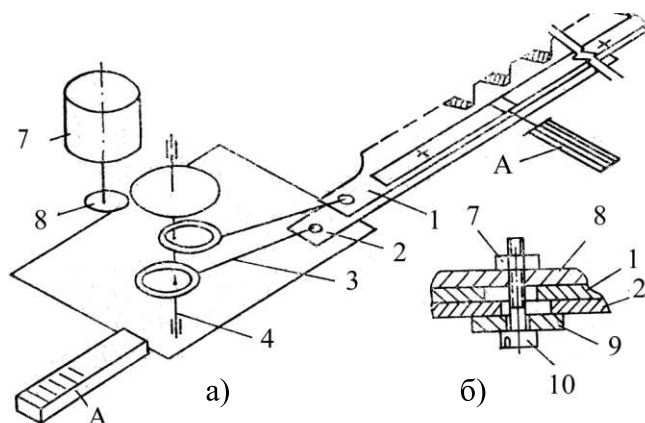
Моторные ножницы для обрезки кустарника: а – кинематическая схема; б – шарнирное соединение ножей; 1 – верхний нож; 2 – нижний нож; 3 – шатун; 4 – эксцентриковый вал; 5 – зубчатая передача; 6 – электродвигатель; 7 – контргайка; 8 – брус; 9 – шайба; 10 – винт
